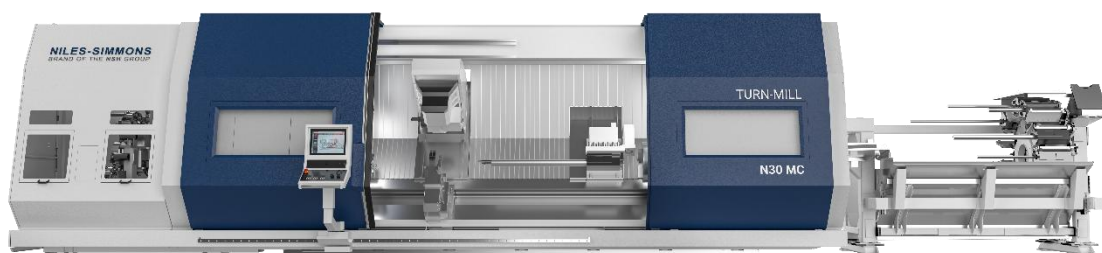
NILES-SIMMONS New Generation TURN-MILL in der Ausführung mit Bohrstangenschlitten und Bohrstangenmagazin für die komplexe Innenbearbeitung
